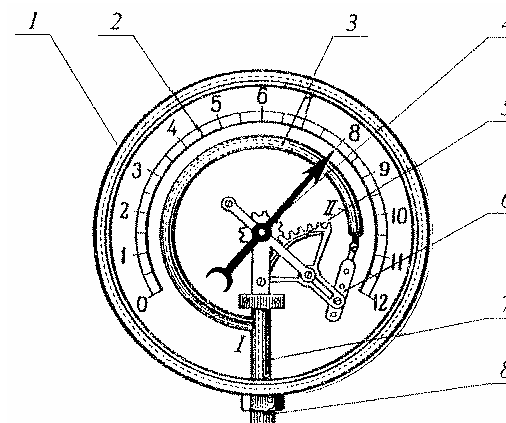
Металлический манометр: 1 – корпус; 2 – шкала; 3 – трубка; 4 – стрелка; 5 – зубчатый сектор; 6 – поводок; 7 – стойка; 8 – патрубок
